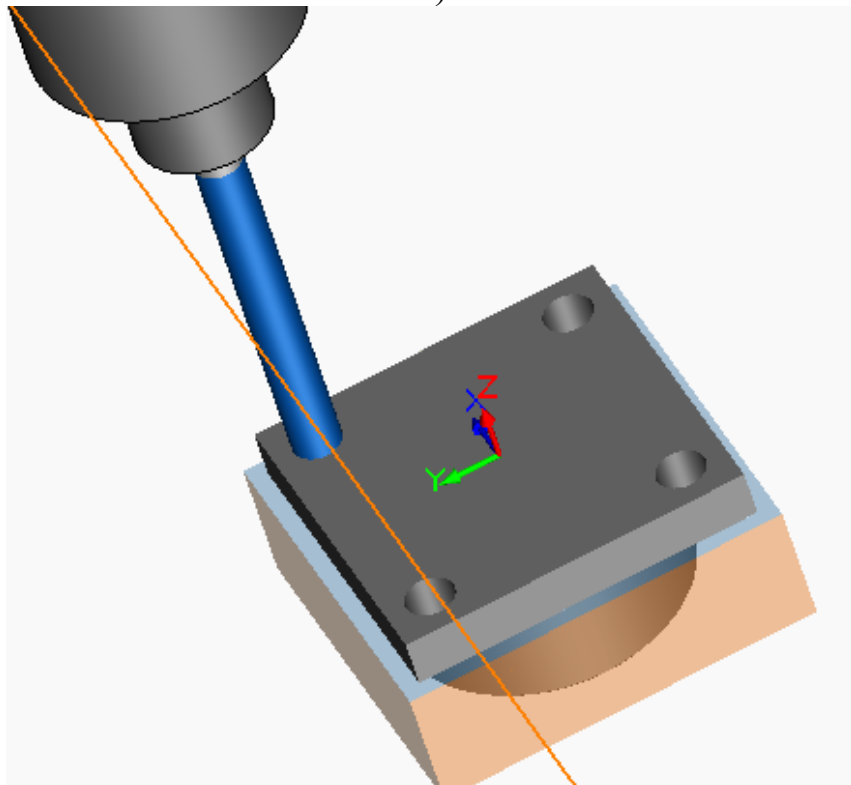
Симуляція обробки деталі на фрезерному верстаті з ЧПК (Свердління отворів поверхня 7)
